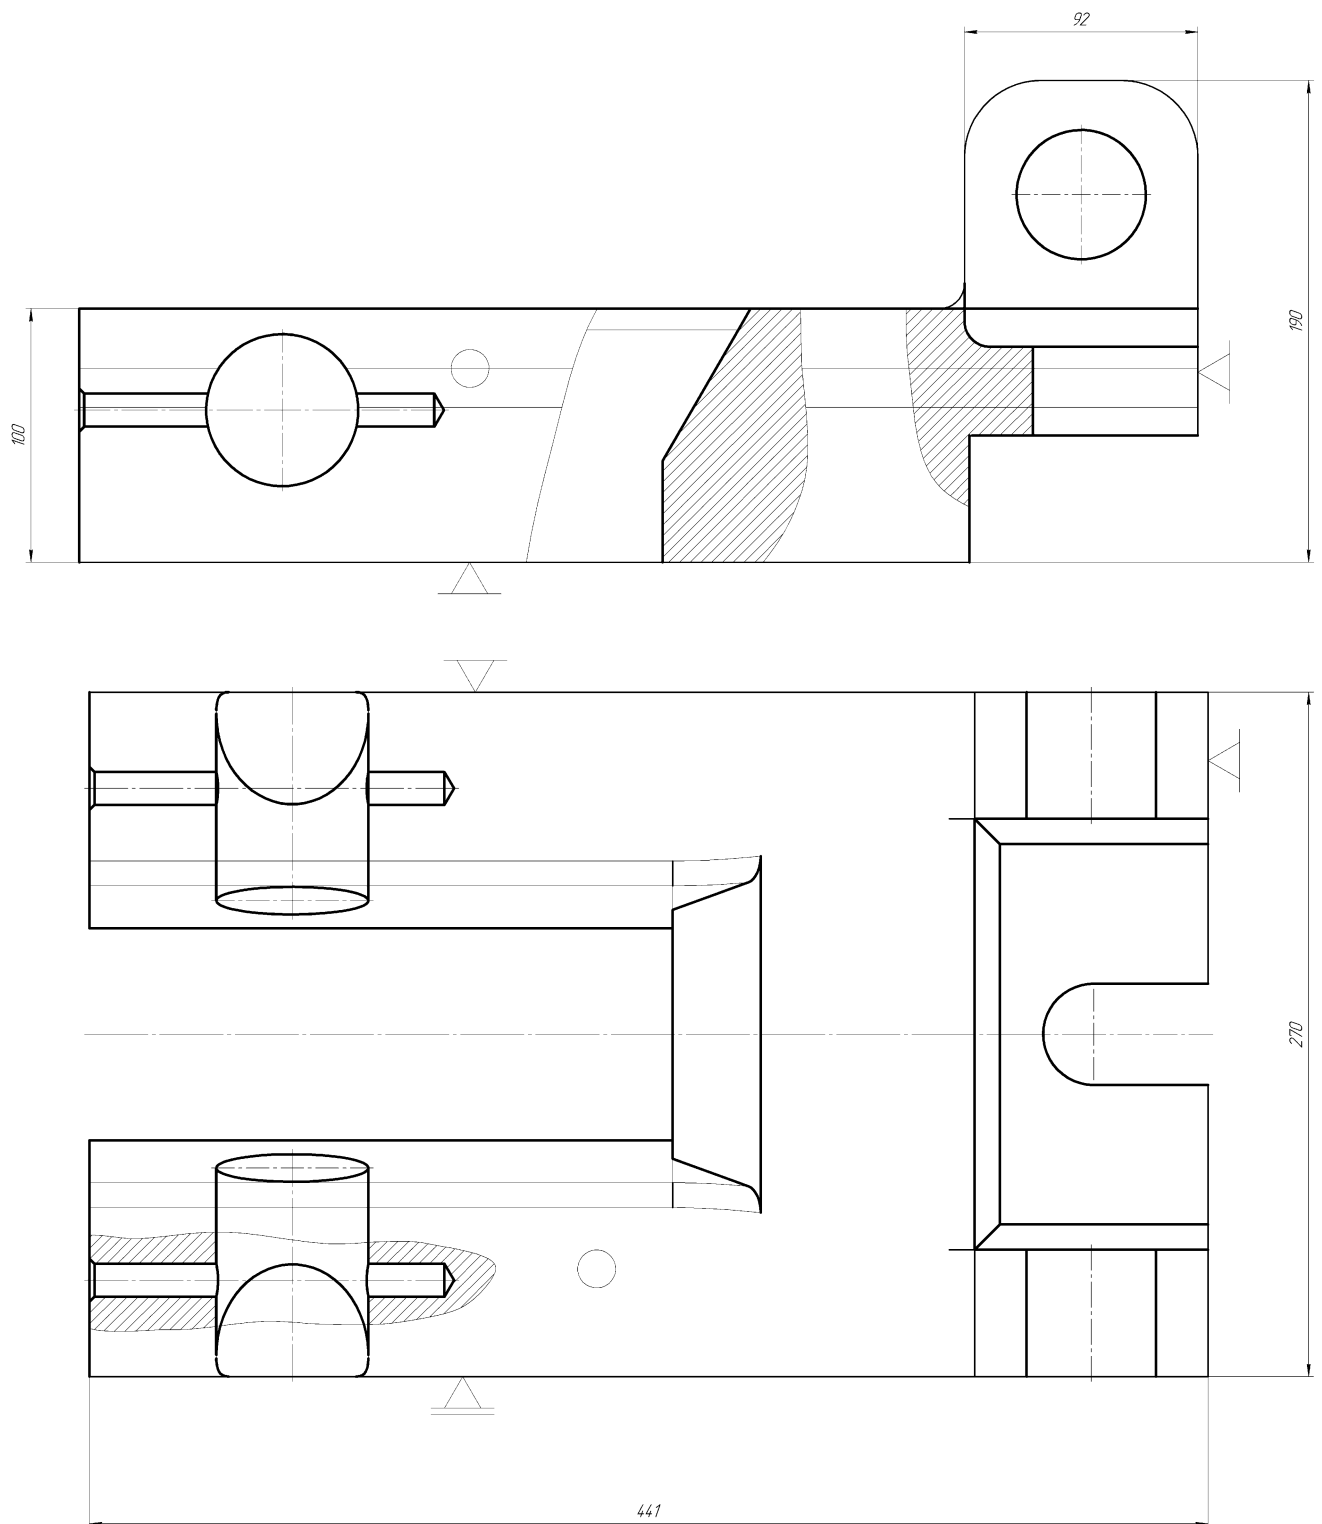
Умовна схема базування на фрезерній операції, установ Б
